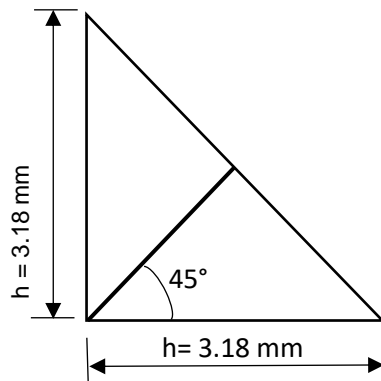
Vista lateral del cordón de soldadura.
